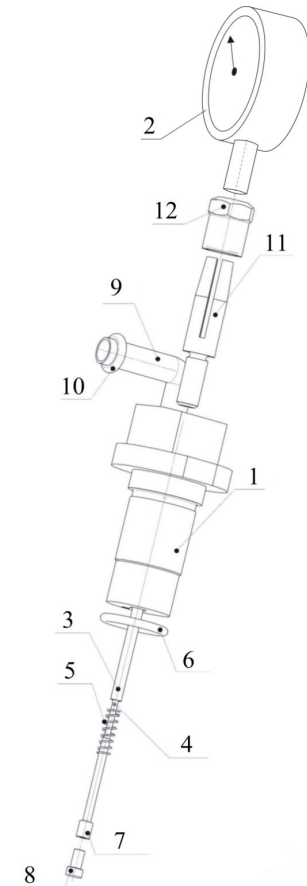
Измерительное устройство для определения зазора в шатунном подшипнике коленчатого вала
